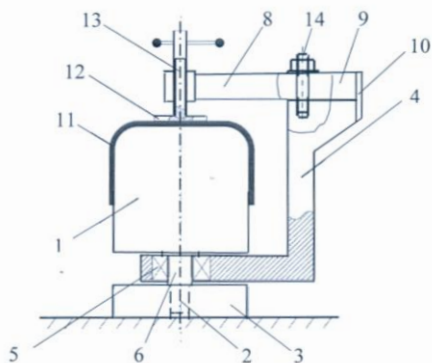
Прижимное устройство для закрепления листовой заготовки на оправке при формообразовании полых деталей способом обкатки: 1- оправка; 2- шип; 3- основание; 4- струпщина; 5-радиально упорный подшипник; 6- цапфа; 8- верхний рычаг струпщины; 9 – крепежная часть рычага; 10- накладка; 11- деталь; 12- опорная пята; 13- винт
